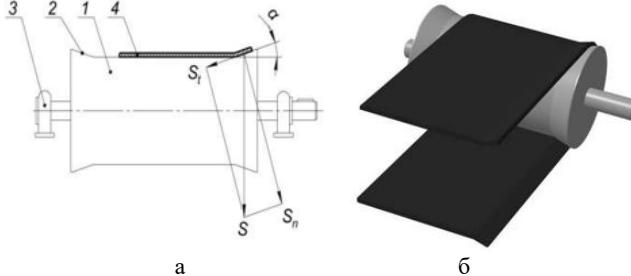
Взаимодействие ленты и барабана ленточного конвейера: а) – схема сил, действующих на ленту конвейера; б) – смещение ленты на центрирующий криволинейный участок барабана; 1 – центральный цилиндрический участок; 2 – торцевой участок; 3 – подшипниковый узел; 4 – лента
